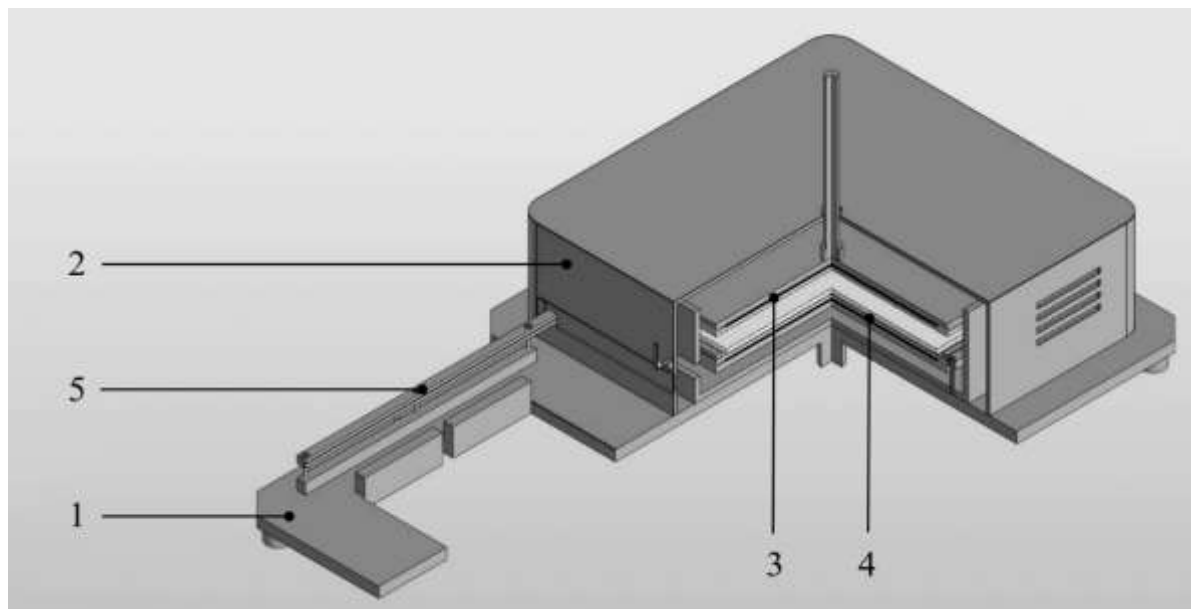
3D модель оснастки: 1 – основание с отверстием для рупоров; 2 – внешний кожух; 3 – верхний нагреватель; 4 – нижний нагреватель; 5 – салазки
